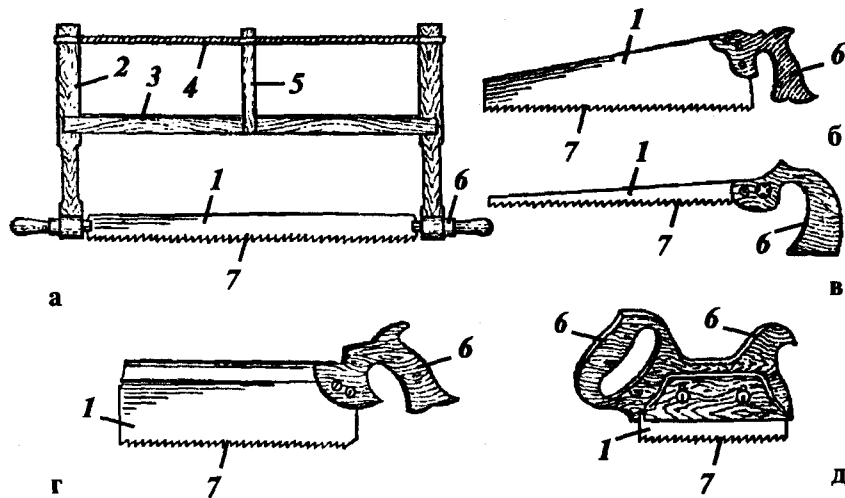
Пилы для выпиливания шиповых соединений: а — лучковая; б — ножовка широкая; в — ножовка узкая; г — обушковая; д — наградка; 1 — полотно; 2 — стойка; 3 — поперечина; 4 — тетива; 5 — закрутка; 6 — ручка; 7 — зубья
